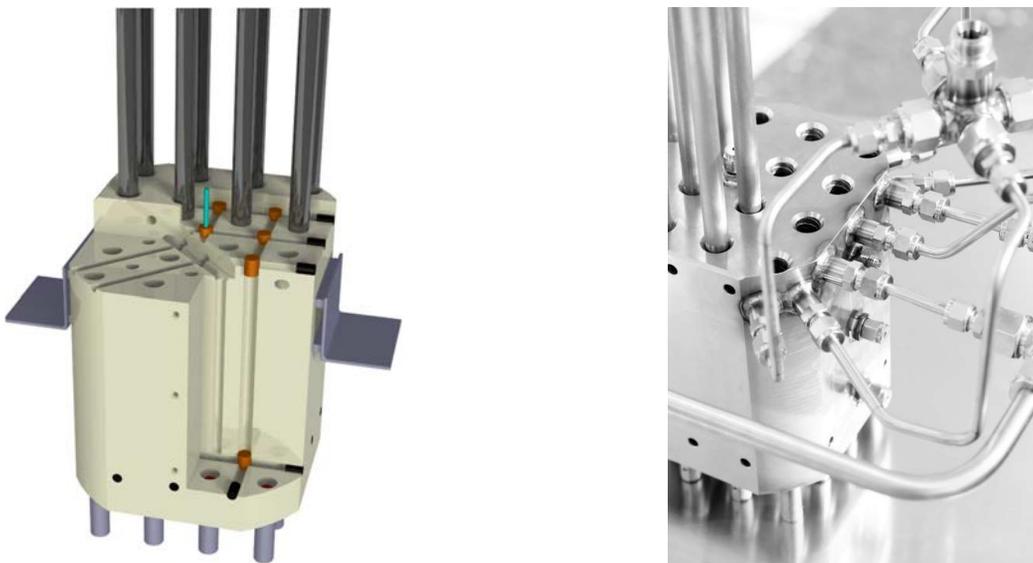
Heatpipe gekühlter Reaktor für die Methanisierung; links: Konstruktion, orange – Sintermetallhülsen, schwarz-glänzend – Heatpipes, schwarz-matt – Schweißstopfen für Verschluss einzelner Bohrungen, rechts: Prototyp
